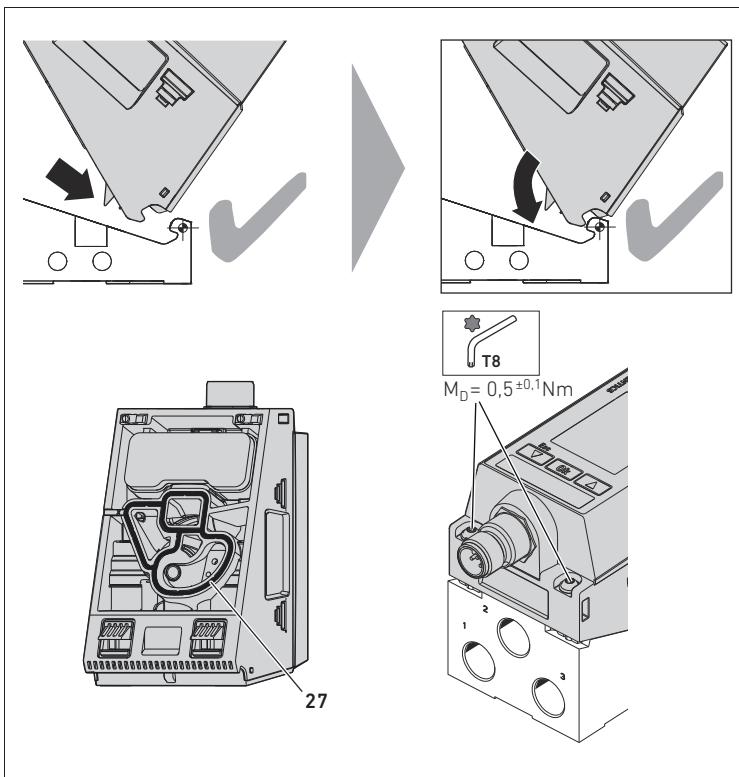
Montaje de la válvula reguladora de presión EV03 en la placa base
